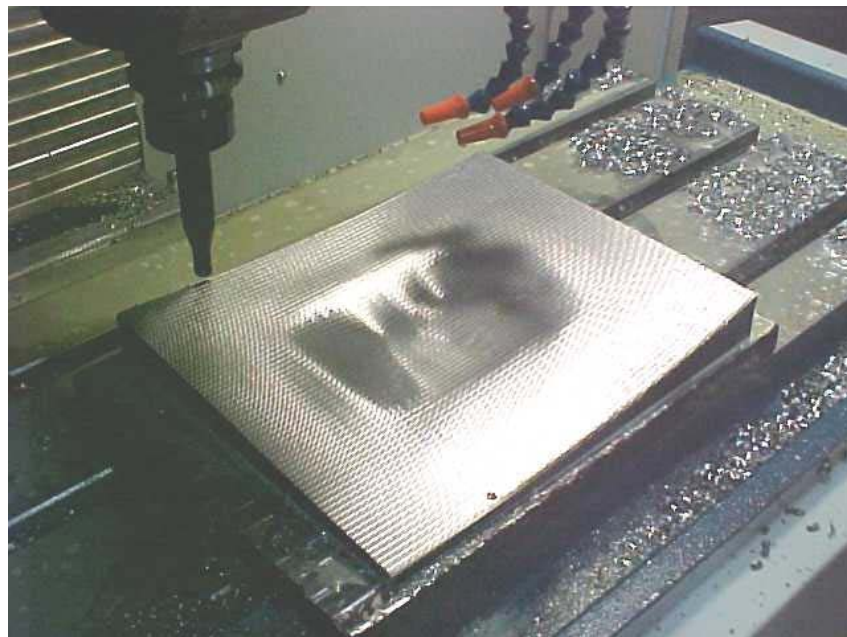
Vista frontal do corpo de prova sendo usinado.
